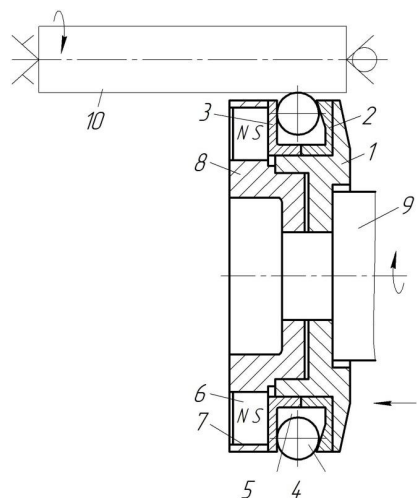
Инструмент для комбинированного магнитно-динамического накатывания поверхности валов
